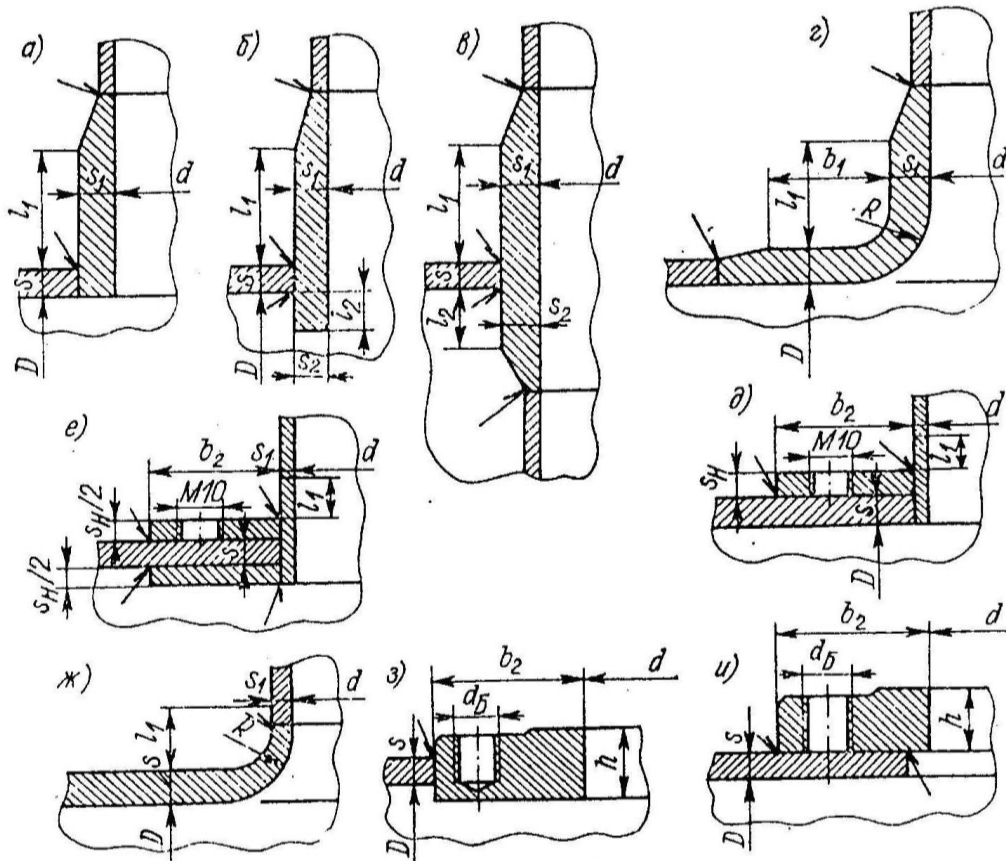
Конструкции укреплений отверстий в стенках сварных аппаратов
